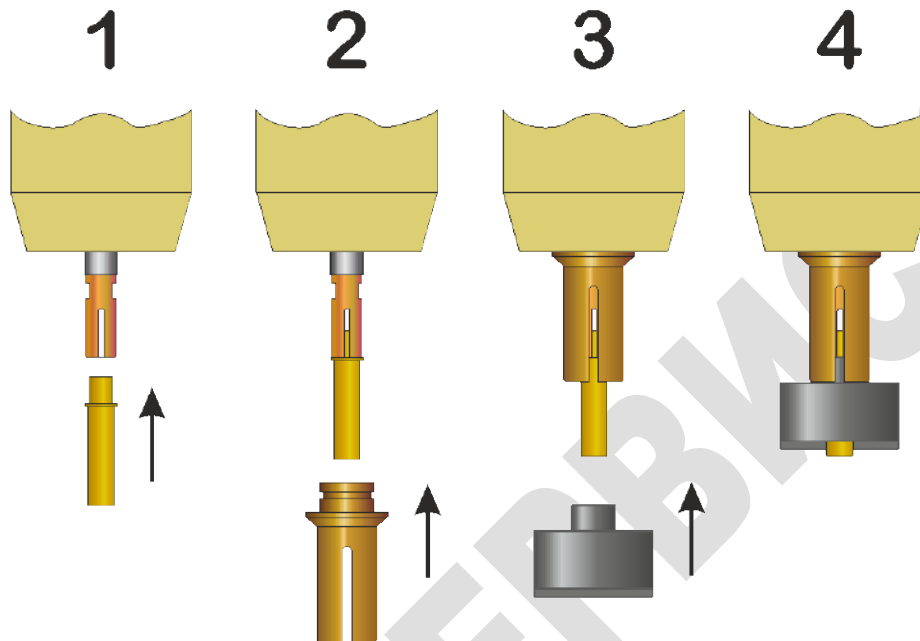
Установка приспособления для проверки расстояния отрыва
